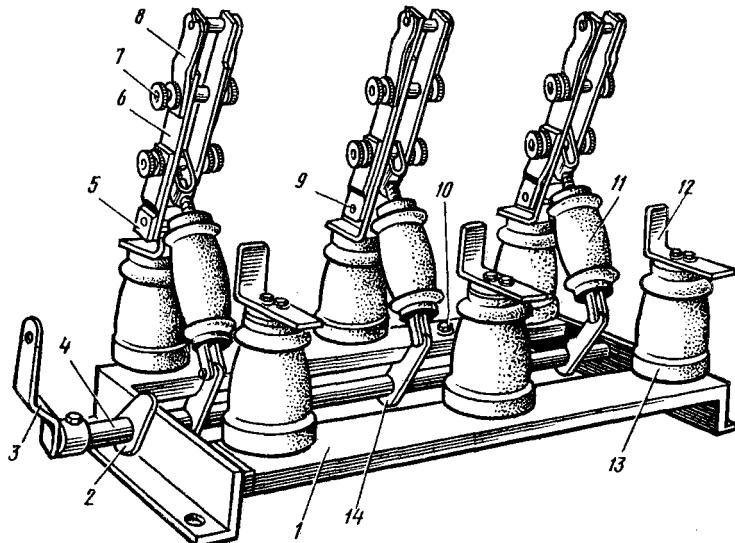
Трехполюсный разъединитель РВ-10/600
